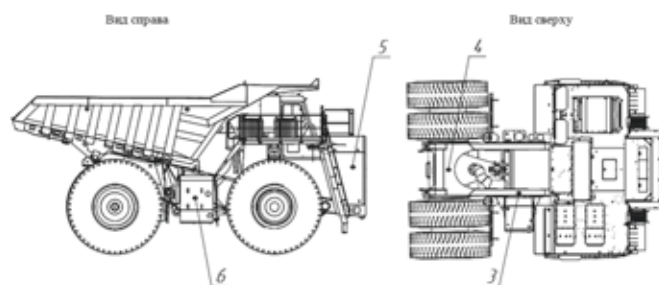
Схема базового размещения стандартного дизельного топливного бака на правом лонжероне рамы карьерного самосвала «БелАЗ-75306»: 3 – правый лонжерон; 4 – рама; 5 – карьерный самосвал «БелАЗ-75306»; 6 – стандартный дизельный топливный бак /
